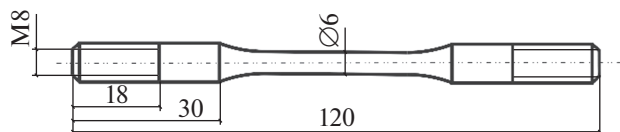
Образец из стали 06X13H5M2Ф для испытаний.
